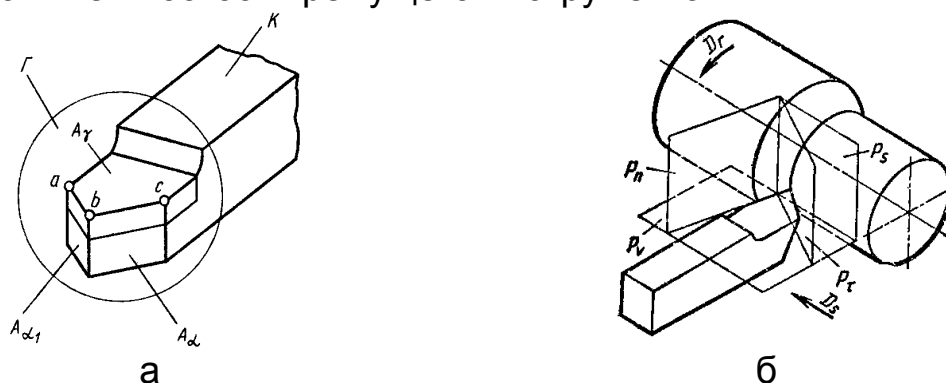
Элементы и координатные плоскости токарного резца
